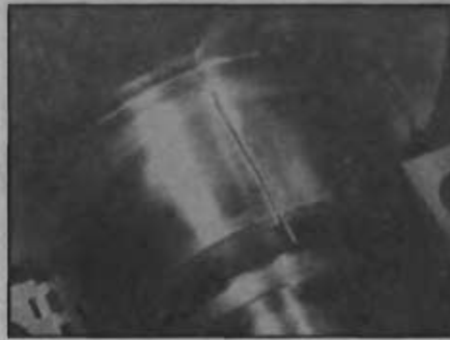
Стержень Plastigauge для измерения зазора в подшипниках, расположенный на шейке коленчатого вала
